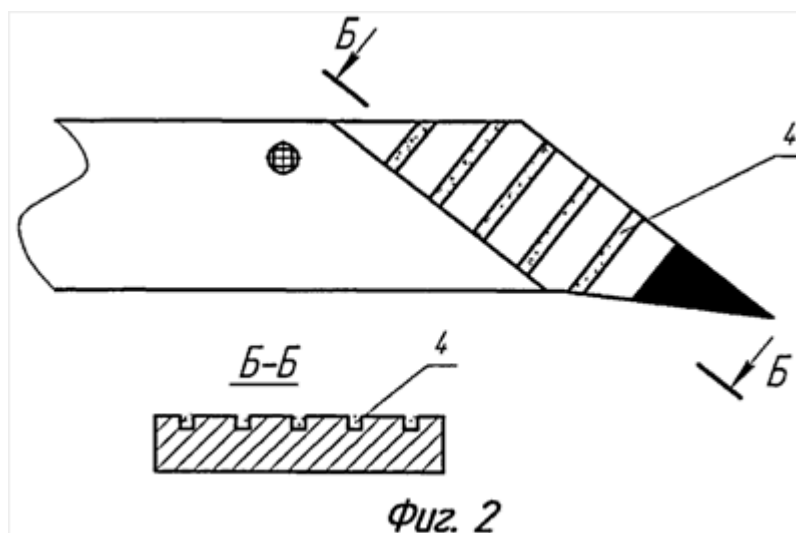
Лемех с пазами, прорезанными в носовой части и с заглавленной заглавливающей частью (1 - рабочая поверхность носка лемеха; 2 - пазы; 3 - наплавленная поверхность; 4 – почвенная масса)
